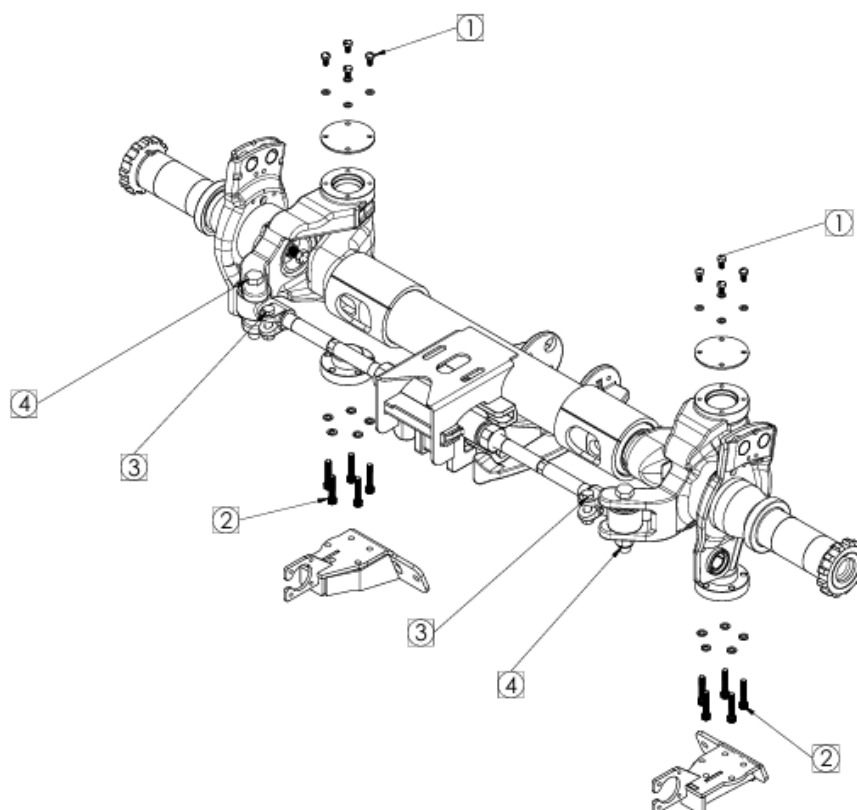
VISTA EXPLODIDA PARA TORQUES.
